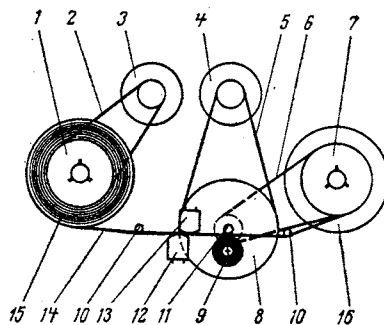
Кинематическая схема магнитофона: 1 — подкатушечник подающего узла; 2, 5 и 6 — резиновые пассивы; 3 — электродвигатель; 7 — подкатушечник приемного узла; 8 — маховик ведущего вала; 9 — прижимной ролик; 10 — направляющие стойки; 11 — ведущий вал; 12 — стирающая головка; 13 — универсальная головка; 14 — магнитная лента; 15 — подающая катушка; 16 — приемная катушка.
